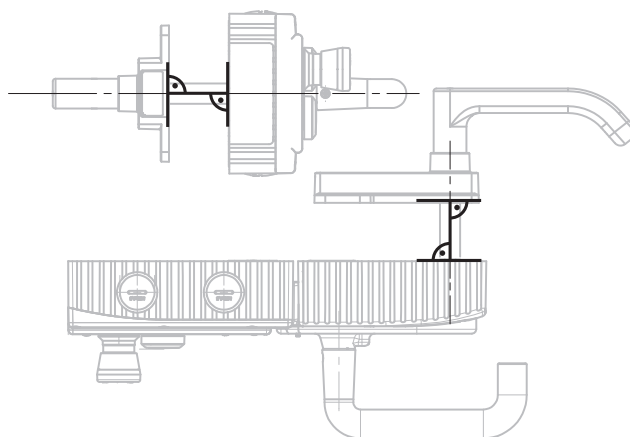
Exemple de montage pour une porte sur charnières à droite (vue d'ensemble)
